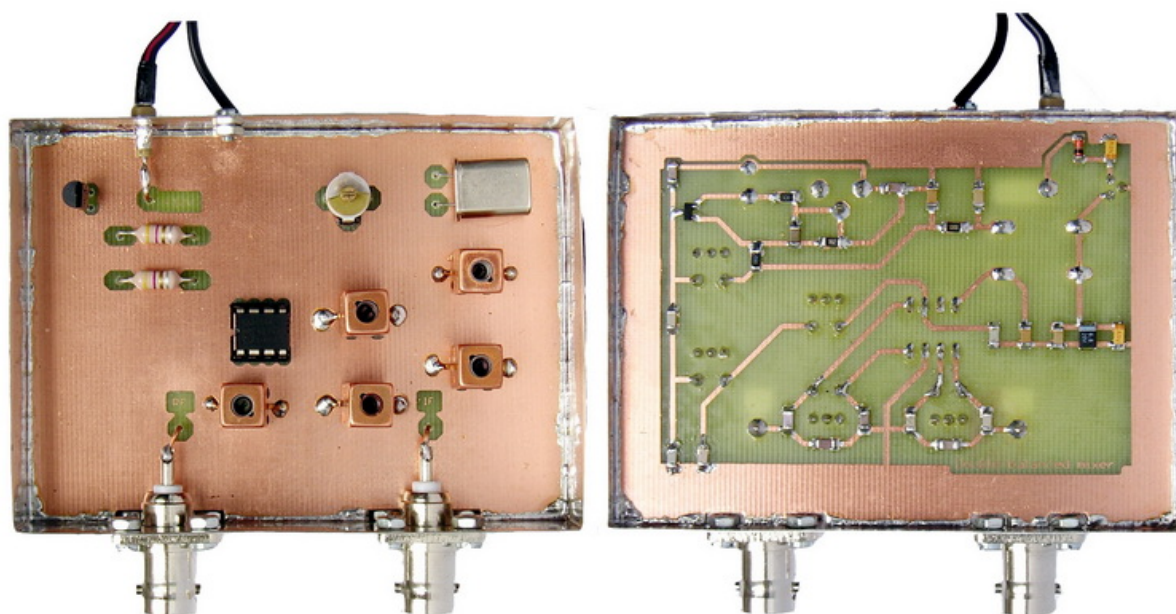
Spodní strana desky přípravku pro měření IP_3 (1:1).
